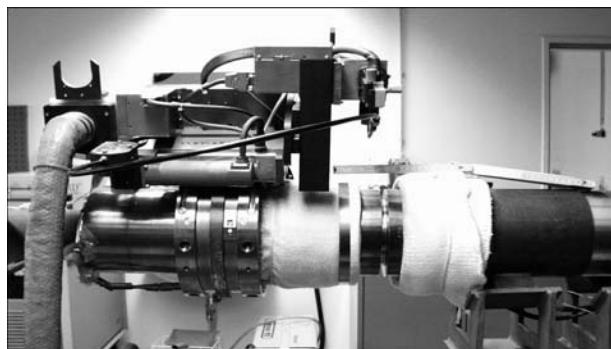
Оборудование для орбитальной сварки в узкий зазор [24]
